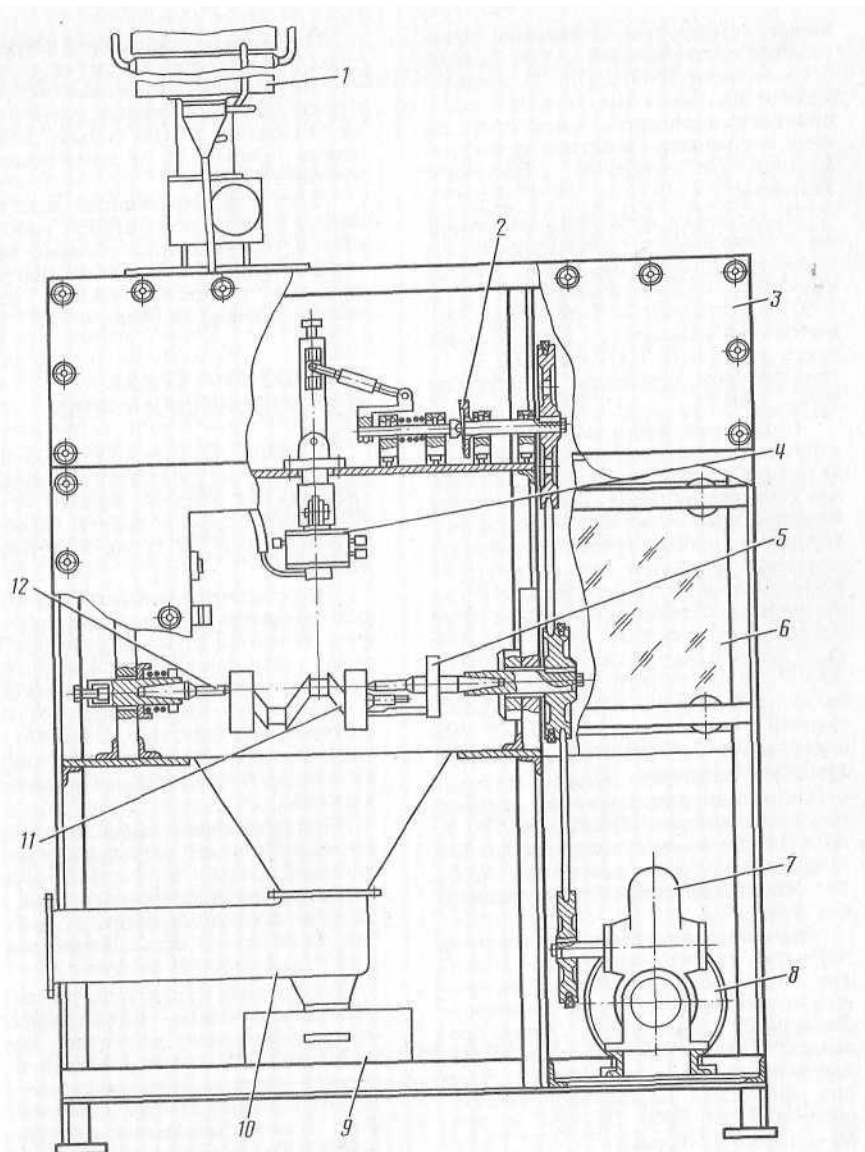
Стенд-камера для напыления наружных цилиндрических поверхностей деталей:
